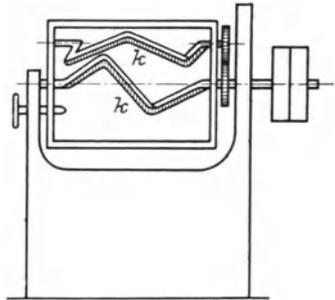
Schema einer Knetmaschine mit gekipptem Knettrug.
